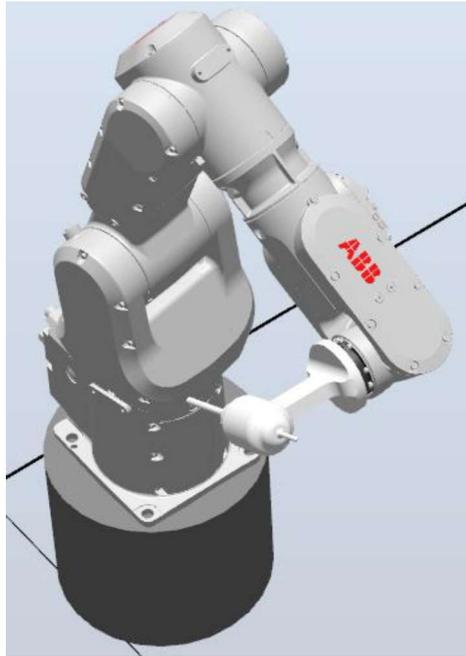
Estación 2, taladradora. Fuente: elaboración propia
